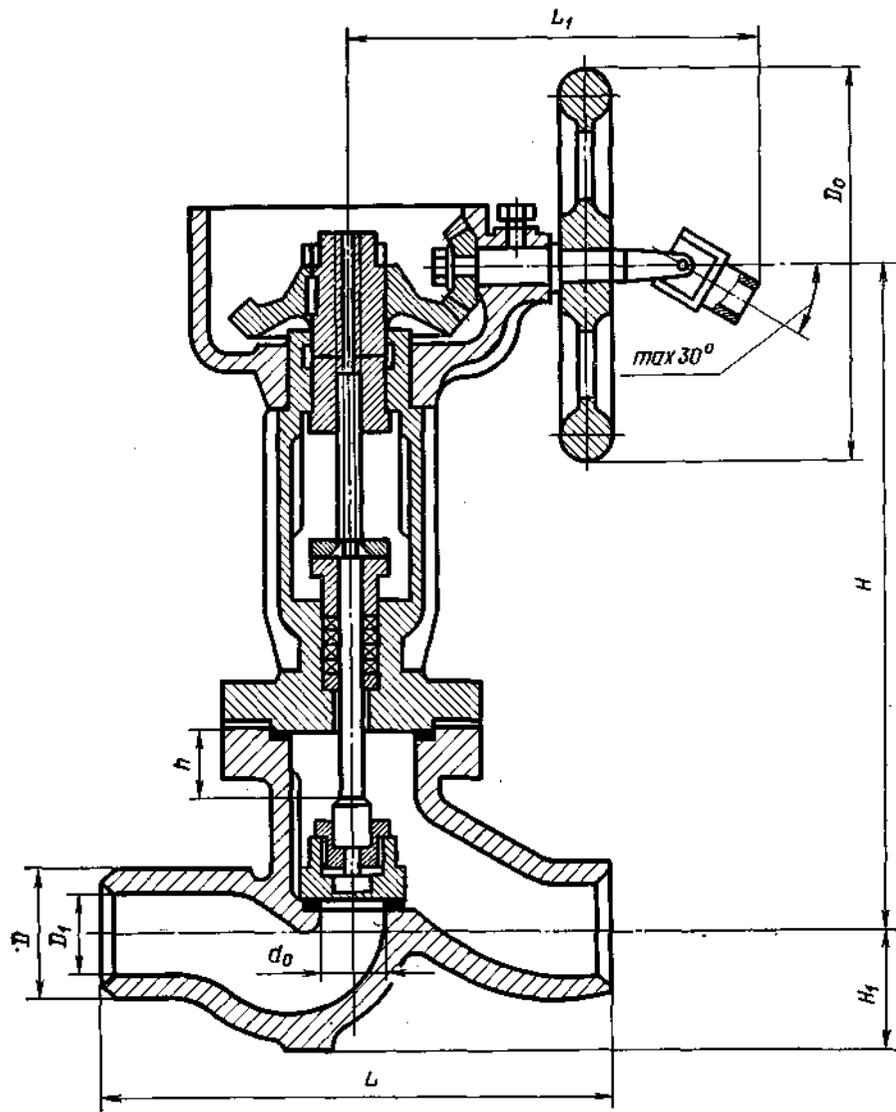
Вентили Т-1086, Т-1116 и Т-1146 с приводной головкой и конической зубчатой передачей D , 50, 100, 150
